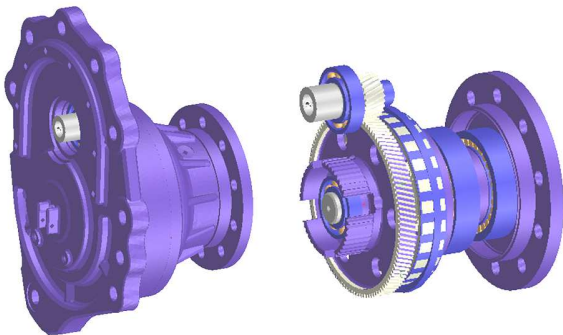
Модель редуктора з корпусом (ліворуч) та без корпусу (праворуч) [37]
